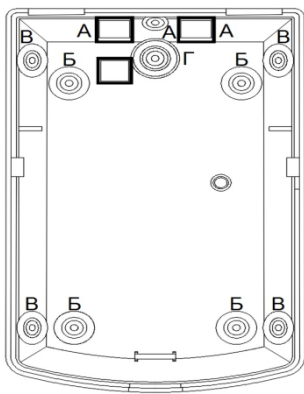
Внешний вид внутренней стороны основания корпуса извещателя
